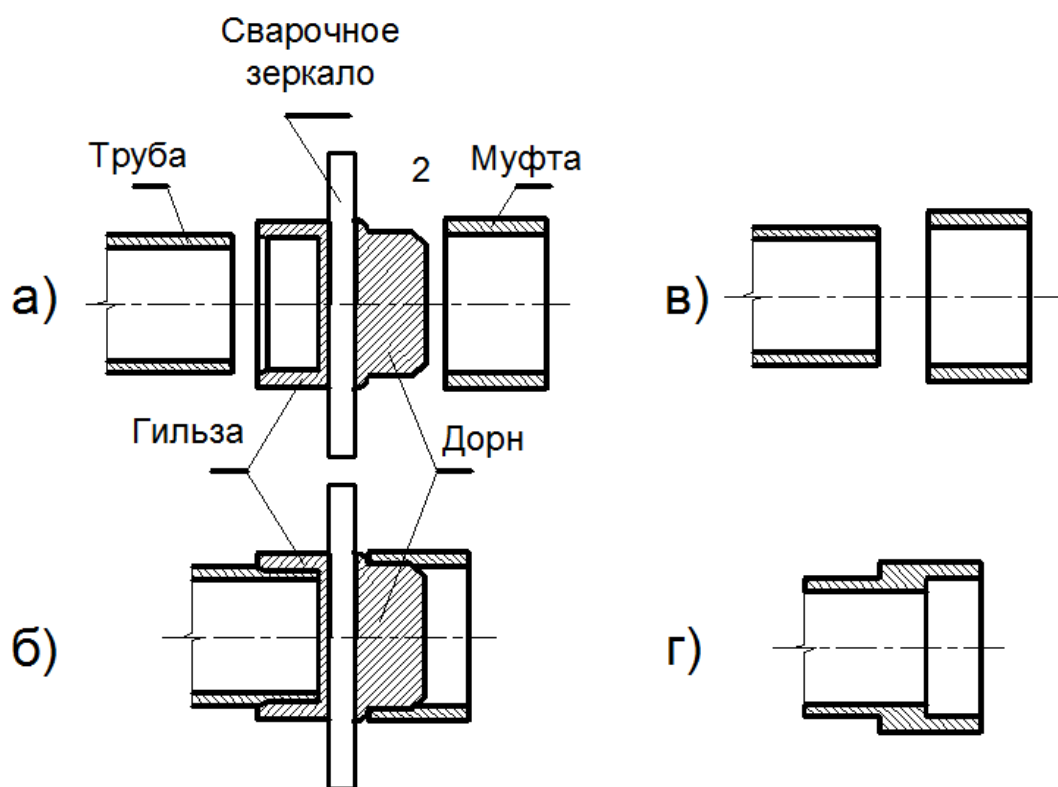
4 - Этапы проведения сварки нагретым инструментом в раструб полимерных труб: а) Нагрев инструмента и подготовка свариваемых трубы и муфты; б) Оплавление гильзой трубы и муфты дорном; в) Технологическая пауза; г) Сварное раструбное соединение
